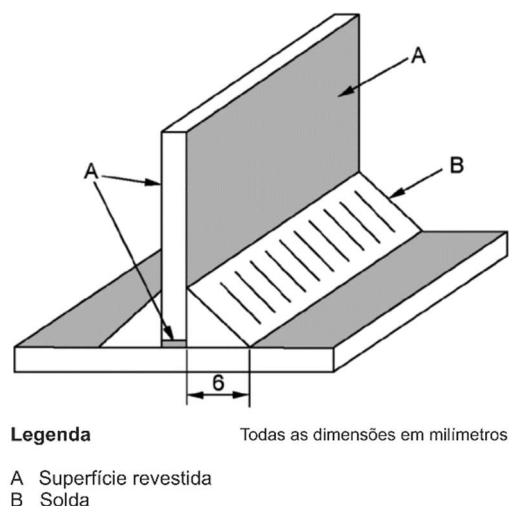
Junta e posicionamento para soldagem – teste de soldabilidade (ISO 17652-2:2003).
